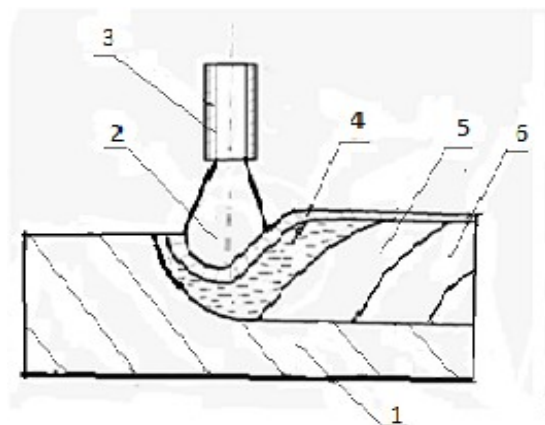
Схема процесу ручного дугового зварювання; 1- основний метал; 2 - дуга; 3 - електрод, що плавиться; 4 – розплав ванни; 5 - плівка розплавленого флюсу; 6 - метал шва
